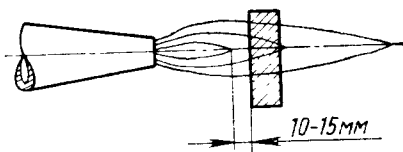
Расположение свариваемого места при сварке природным газом
